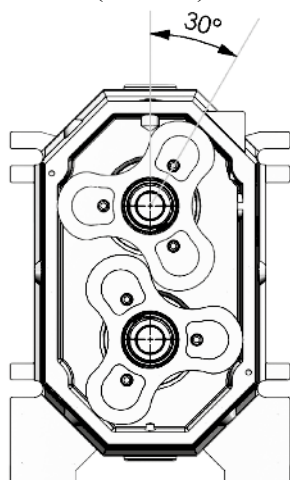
Sequenz Aufschaubung Schrauben auf Verbinder Zahnräder.
